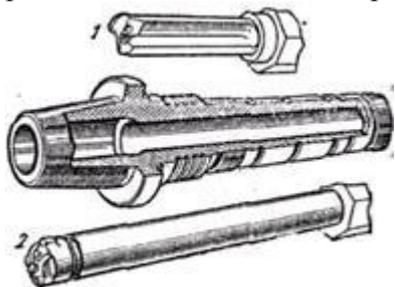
Сверло для глубоких отверстий с пластинками типа «Эжектор»
